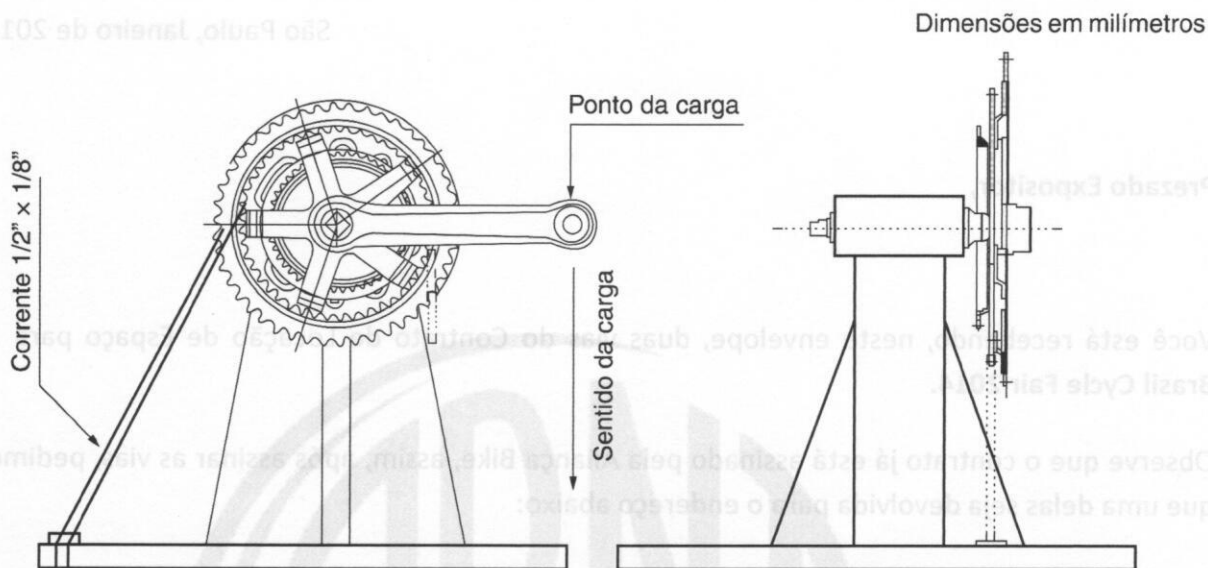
Equipamento de ensaio da pedivela montado com engrenagem com carga estática
